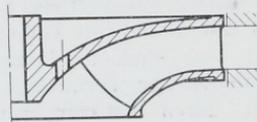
Francisturbine für geringe Laufgeschwindigkeit.
